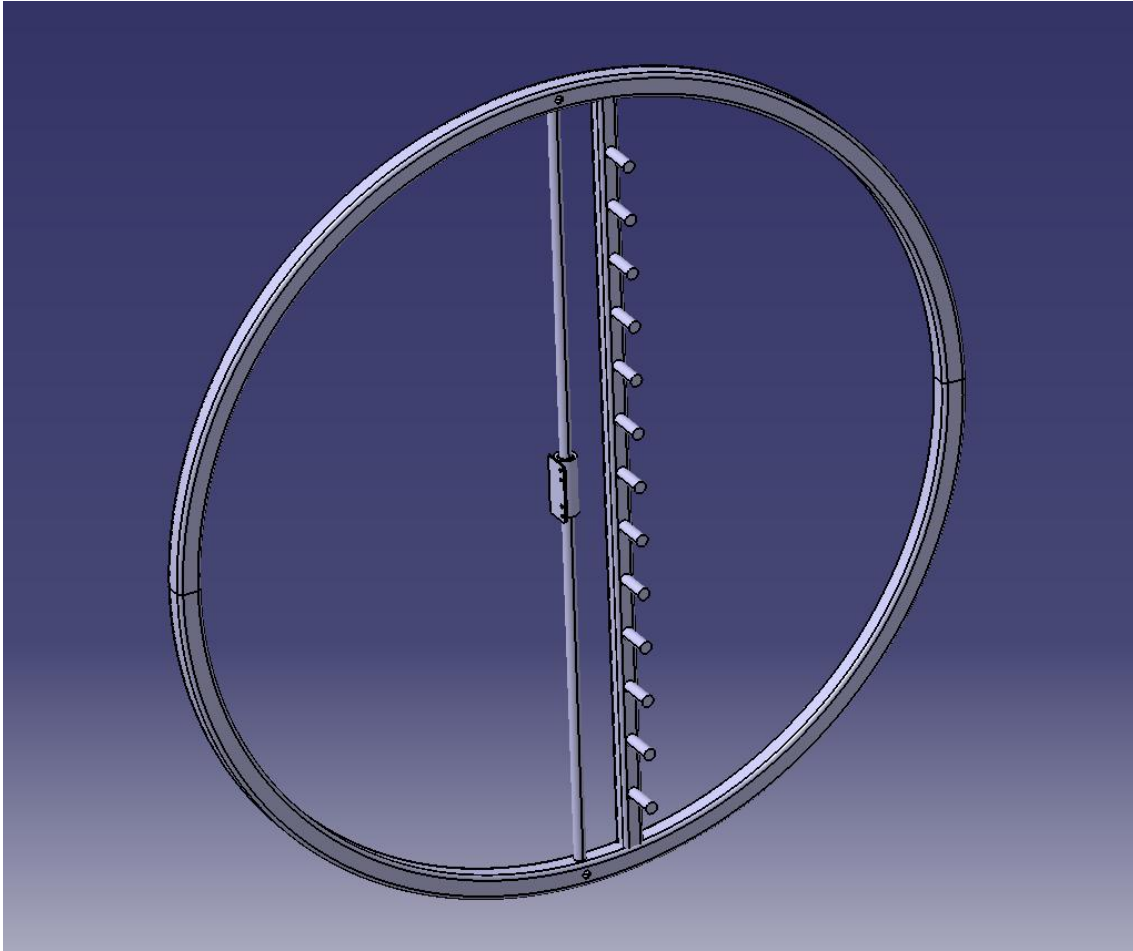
Piezas de giro soldadas con la pieza de giro de la barra
